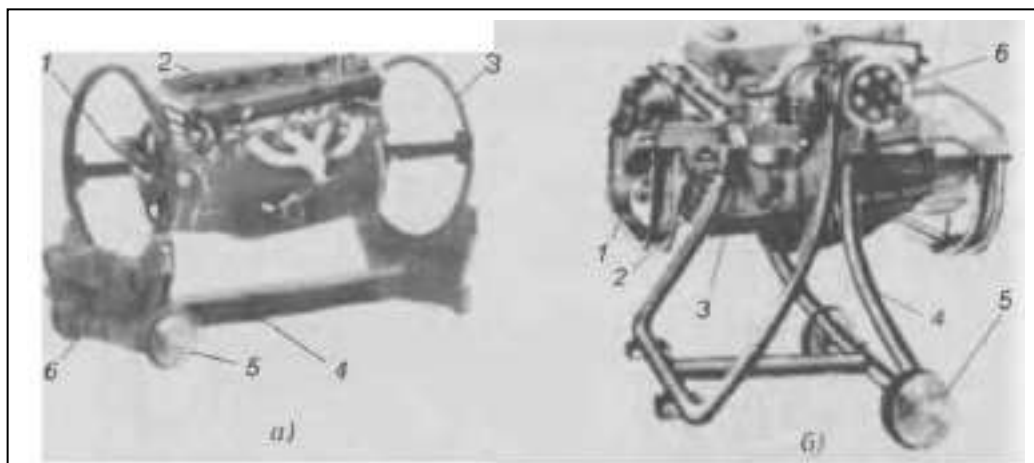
Стенды для разборки и сборки двигателей: *а* — поворотный вокруг продольной оси; *б* — поворотный вокруг поперечной оси; 1 — опора двигателя; 2 — двигатель; 3 — поворотная рукоять; 4 — станина; 5 — колесо; 6 — механизм фиксированного поворота двигателя
